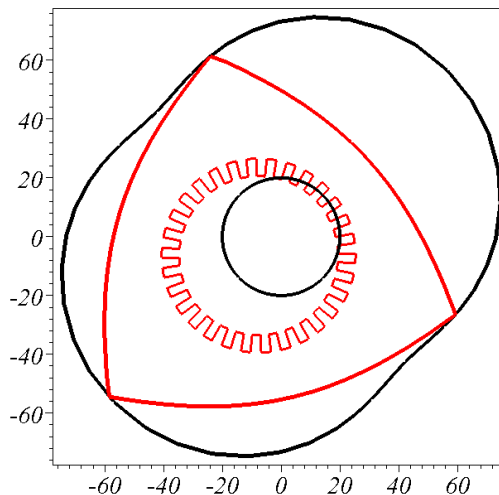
Одна з миттєвих фаз обкатки зубчатым колесом меандрового типу
